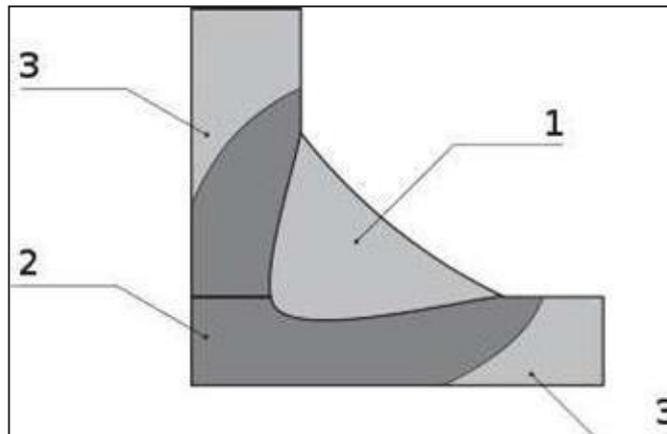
Morphologie d'un cordon de soudure d'angle [5]
